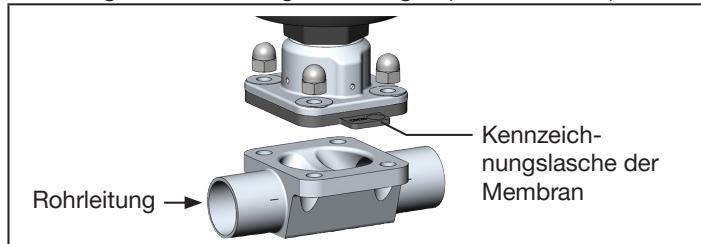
Membran ausrichten (Beispiel 2-Wege-Gehäuse)
